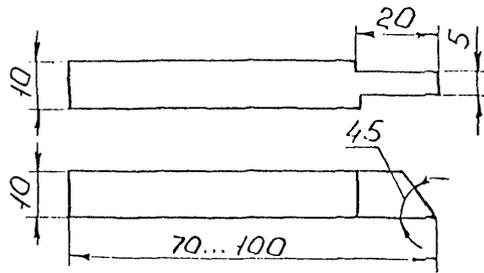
Боек для изготовления искусственных дефектов типа зарубок
